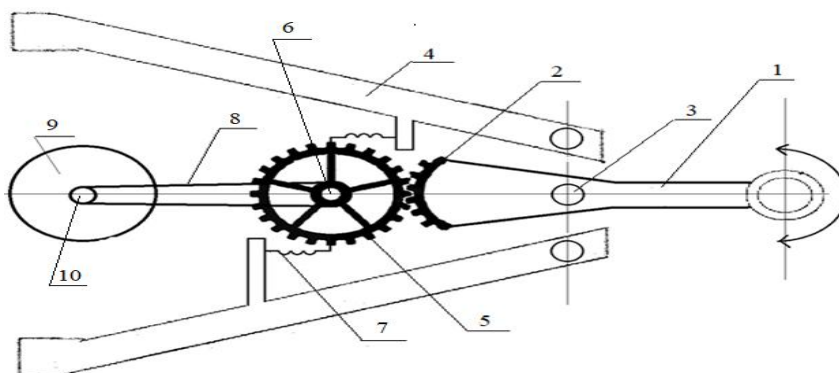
Вид сверху тягово–сцепного устройства:
